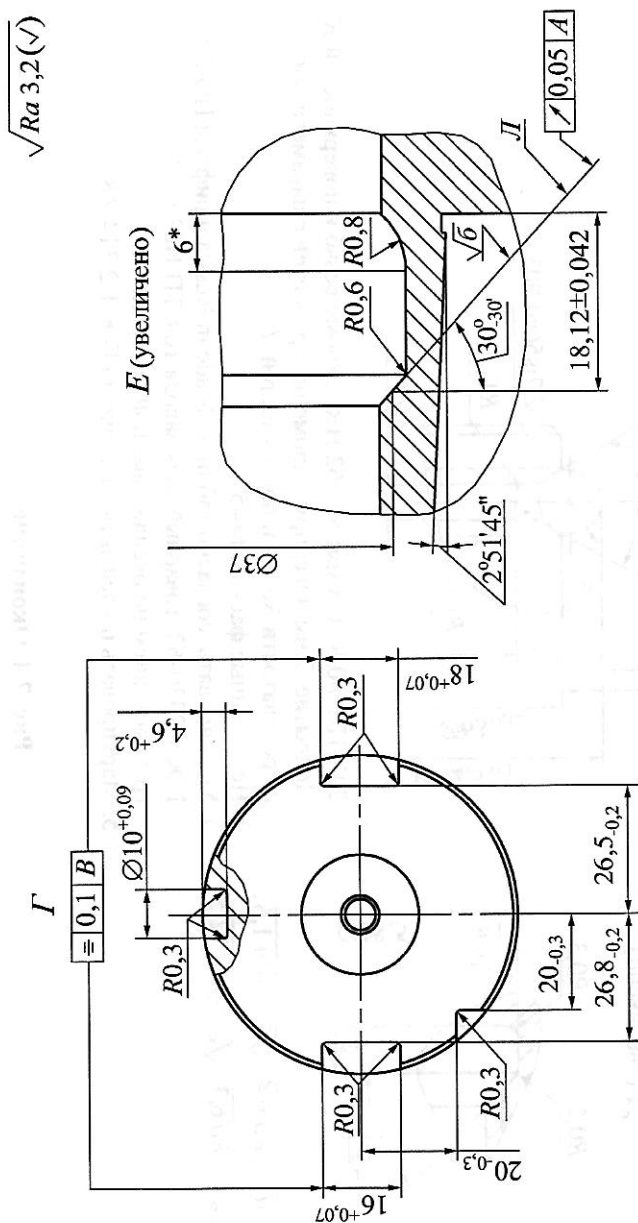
Рабочий чертеж корпуса ВИ с хвостовиком HSK (начало)
